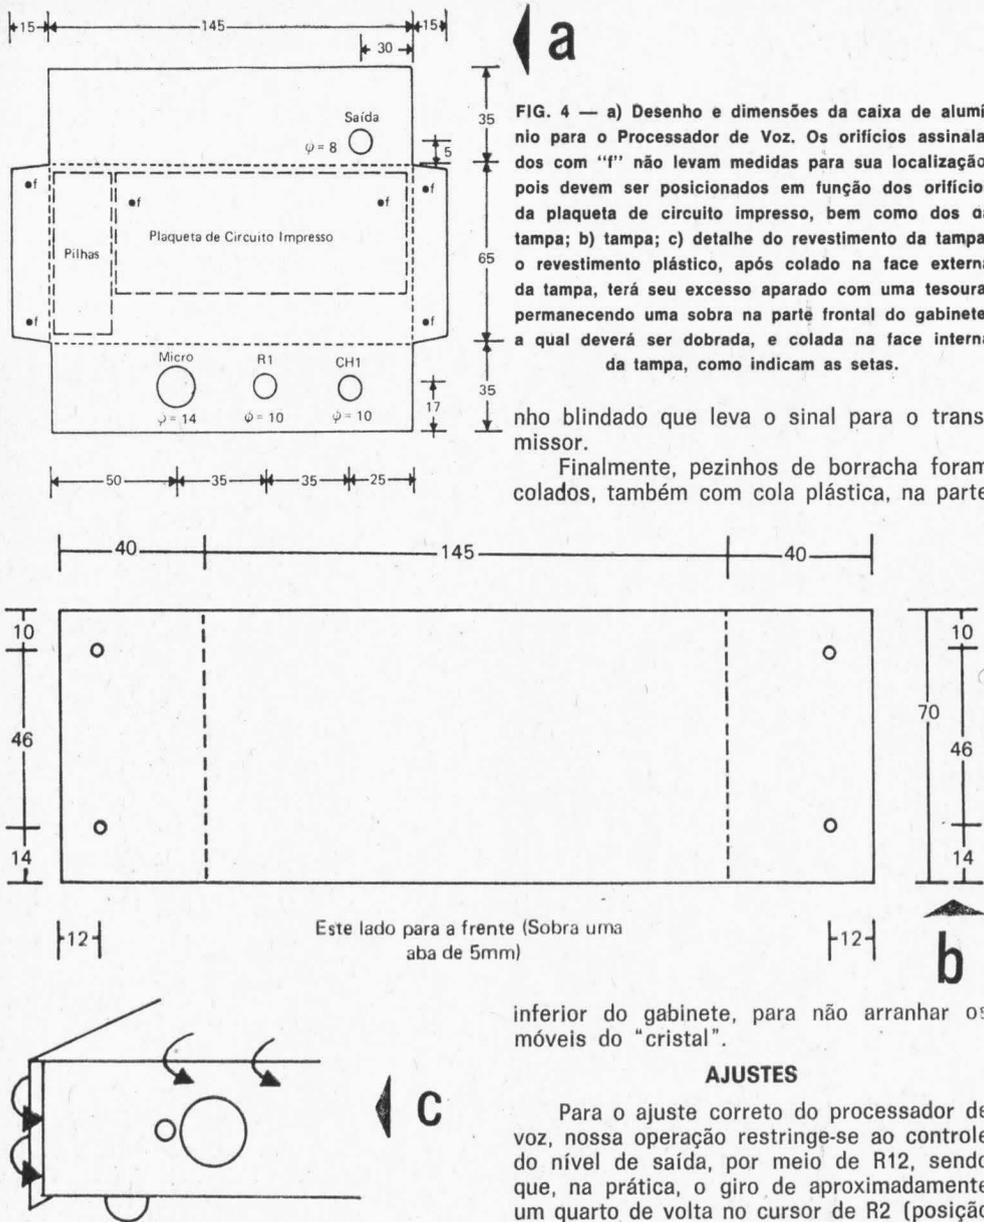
a) Desenho e dimensões da caixa de alumínio para o Processador de Voz. Os orifícios assinalados com "f" não levam medidas para sua localização, pois devem ser posicionados em função dos orifícios da plaqueta de circuito impresso, bem como dos aa tampa; b) tampa; c) detalhe do revestimento da tampa: o revestimento plástico, após colado na face externa da tampa, terá seu excesso aparado com uma tesoura, permanecendo uma sobra na parte frontal do gabinete, a qual deverá ser dobrada, e colada na face interna da tampa, como indicam as setas.
